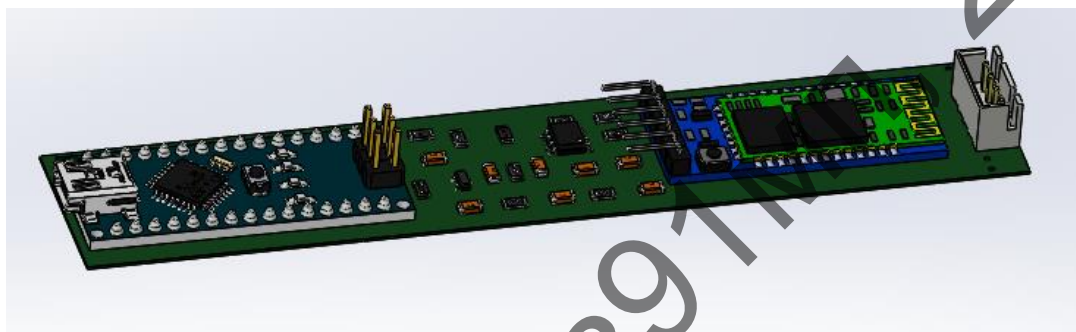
3D модель верхньої частини плати датчику металошукачу
